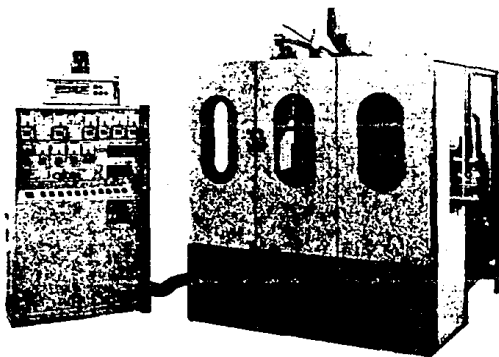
Moldeo por soplado en una máquina de moldeo por inyección dosificada.
